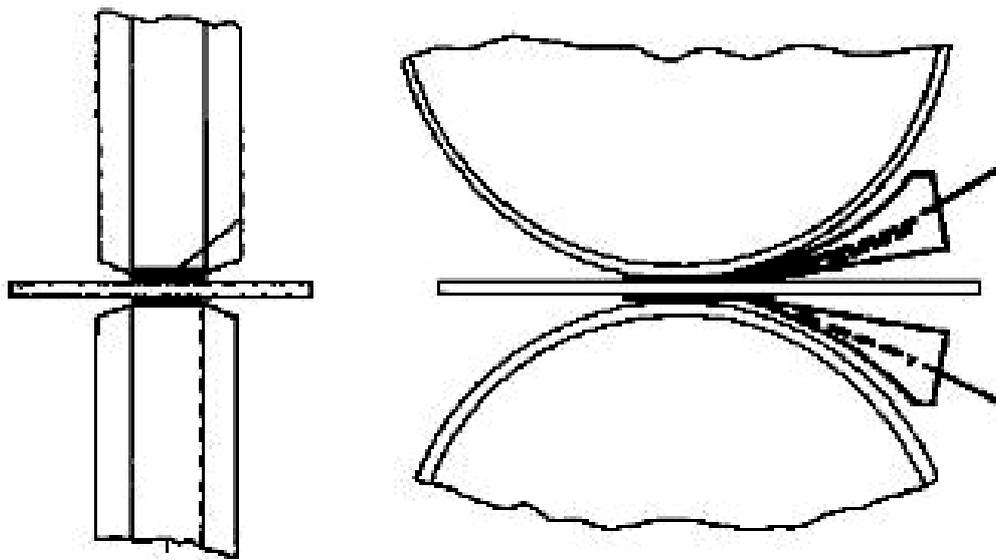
Схема машины для точечной сварки
